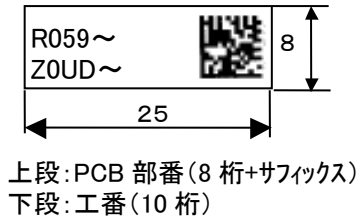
PCB 部番・工番・MAC アドレス ラベル配置図
